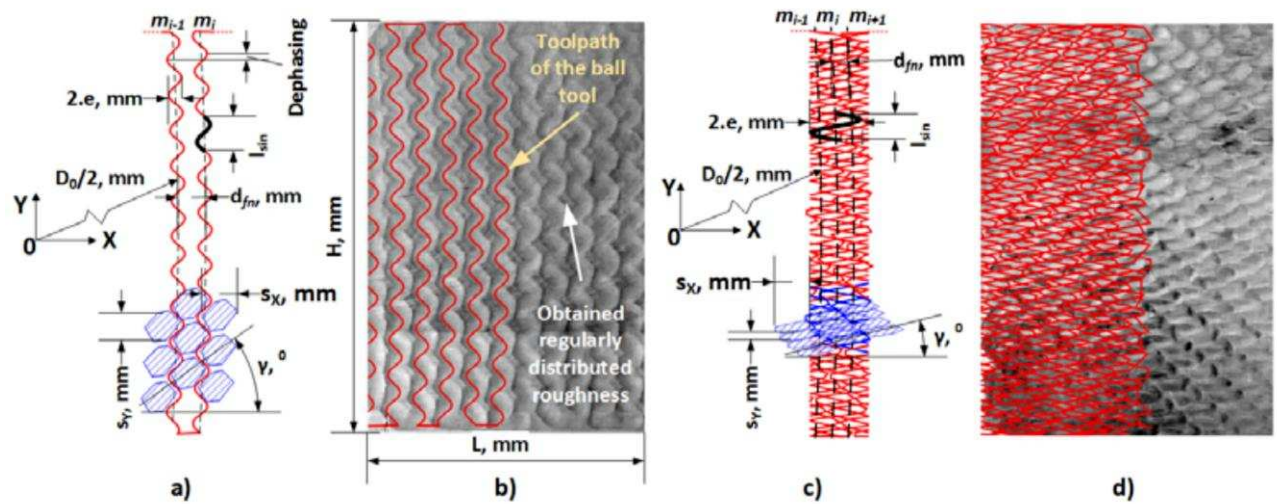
Процес формування регулярного мікрорельєфу на фрезерному верстаті з ЧПК [70]:
